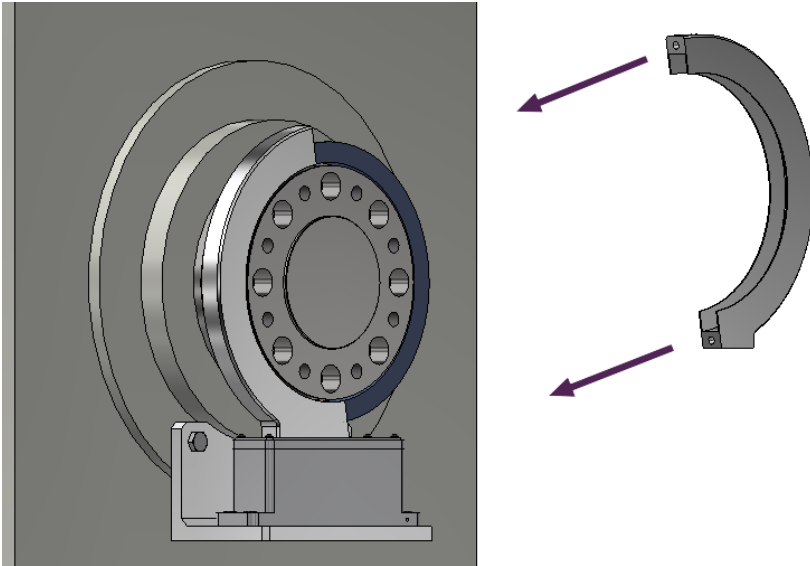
DF ibex/dual - Montage des Metallhalbrings 1
